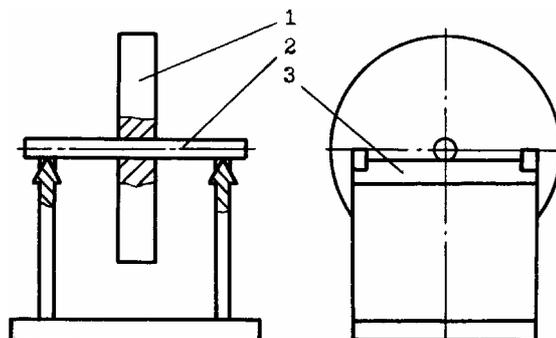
Схема устройства для статической балансировки деталей на призмах:
